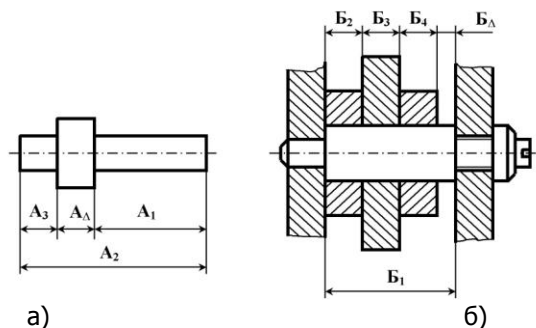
Размерные цепи: а – поддетальная; б – сборочная.
